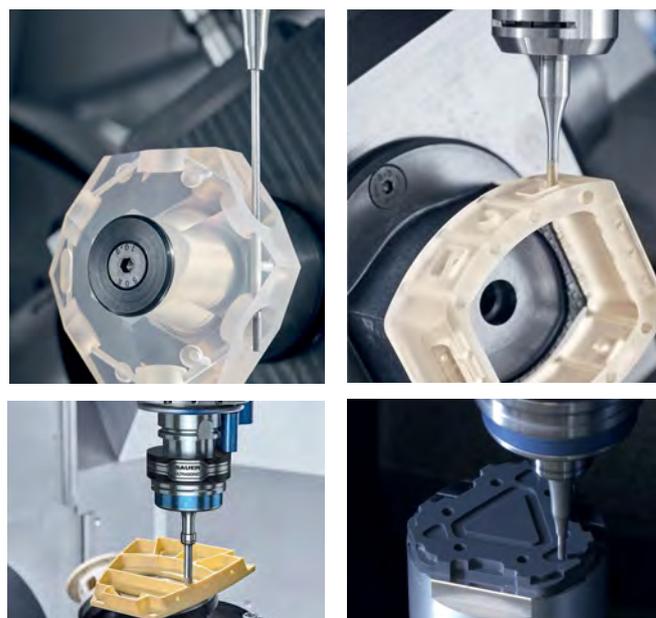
Ультразвуковое фрезерование и сверление изделий из керамик и композитов на станках DMG MORI
